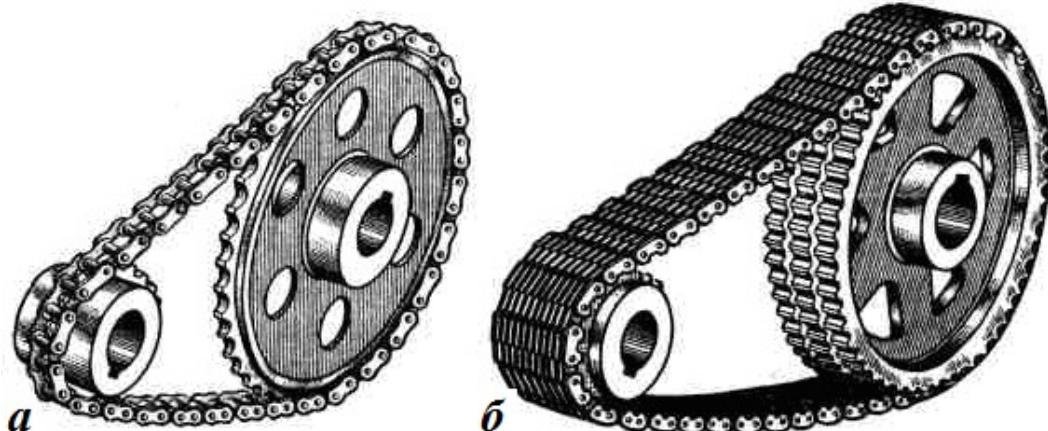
Цепная передача а – роликовой цепью, б – зубчатой цепью
